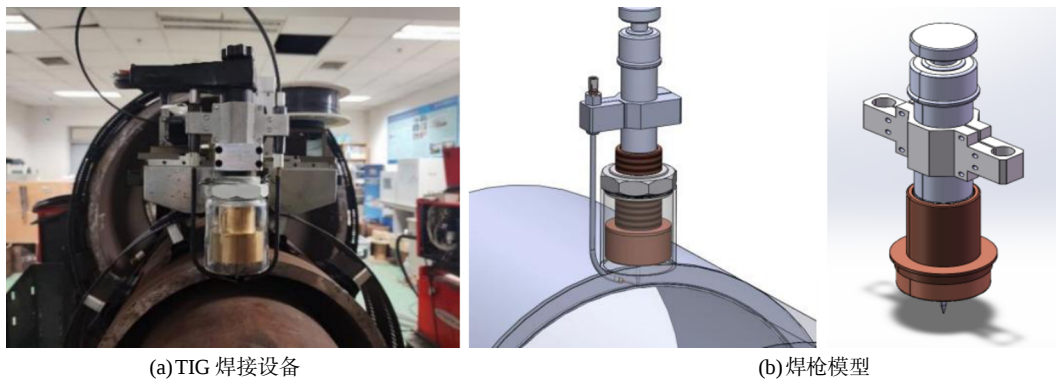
输氢管道用 TIG 焊接设备和焊枪
